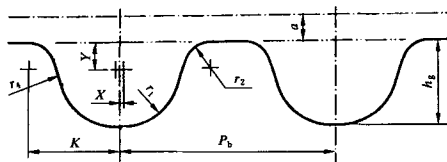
加工 ZH 型带轮的齿条刀具(齿数 17~26)
